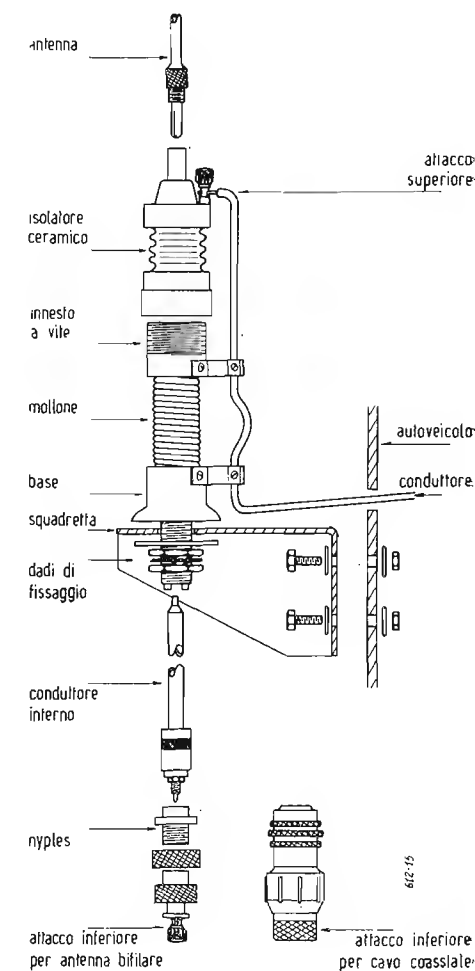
Disegno di montaggio dell'antenna su veicoli.
